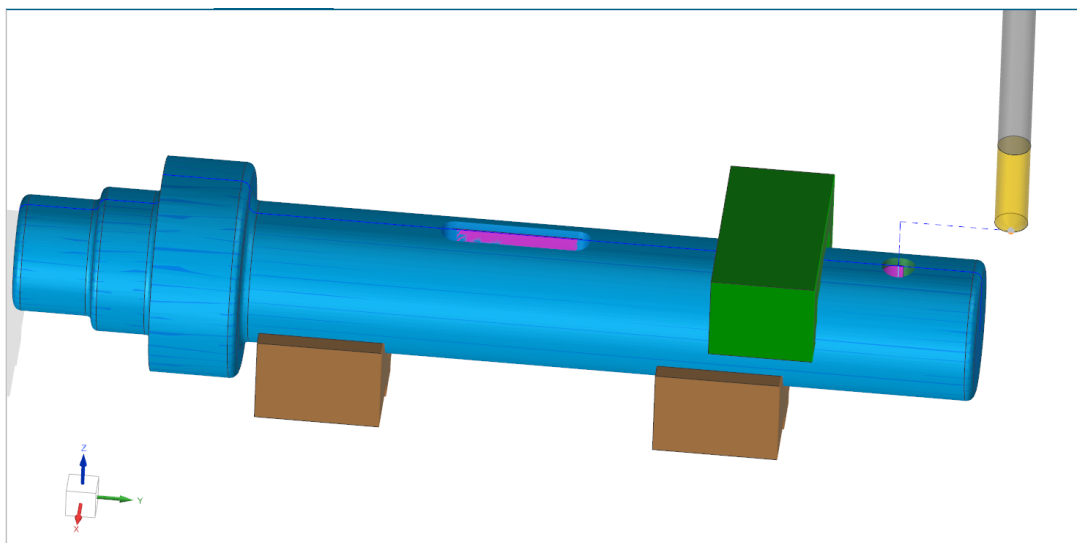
Результат обробки свердильної та фрезерної операцій
